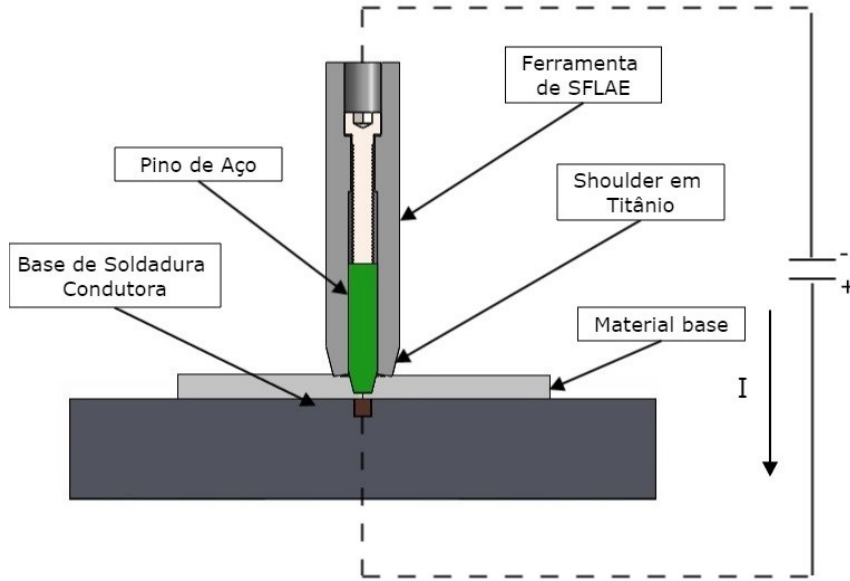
Esquema de soldadura por fricção linear assistida por corrente elétrica para a abordagem tecnológica #3.
